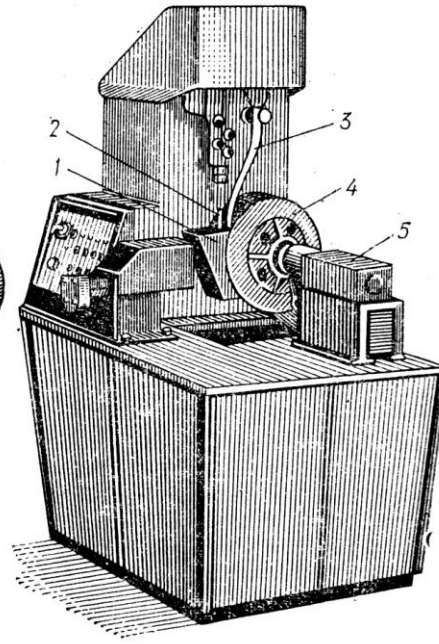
Установка ОКС-7755 для електрошлакового наплавлювання бігової доріжки опорного котка:
